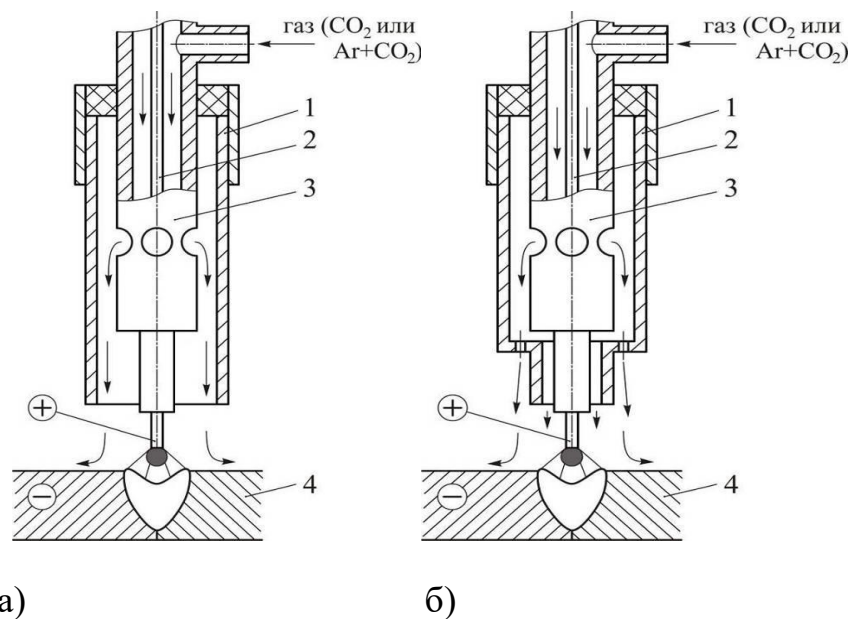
Схема истечения защитного газа из сварочного сопла:
